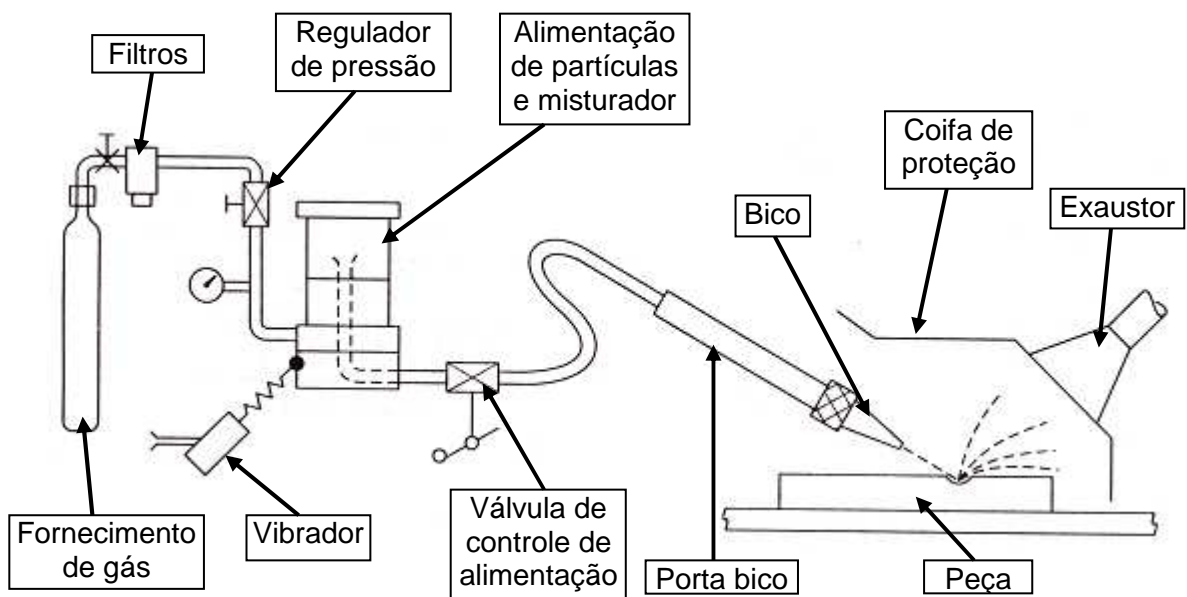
Componentes do sistema de Usinagem por Jato Abrasivo (FULLER, 1989).
